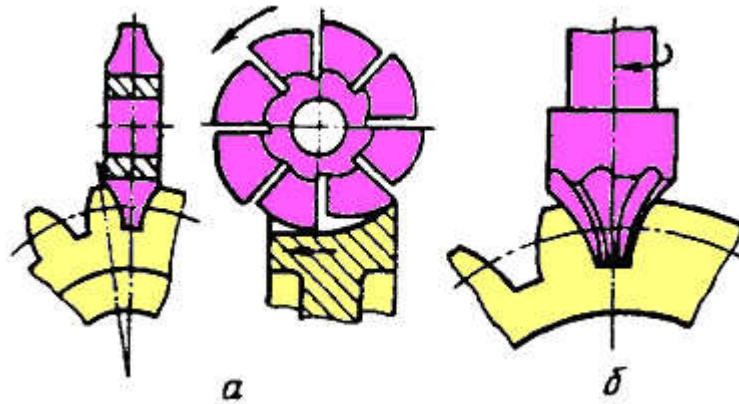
Фрезерование зубьев шестерен модульными фрезами:
